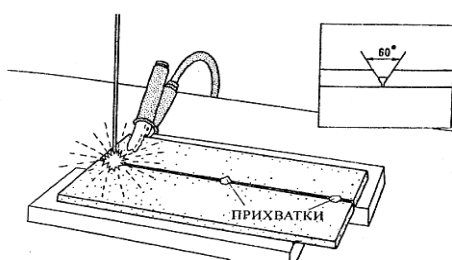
Закрепление элементов фермы короткими сварными швами
